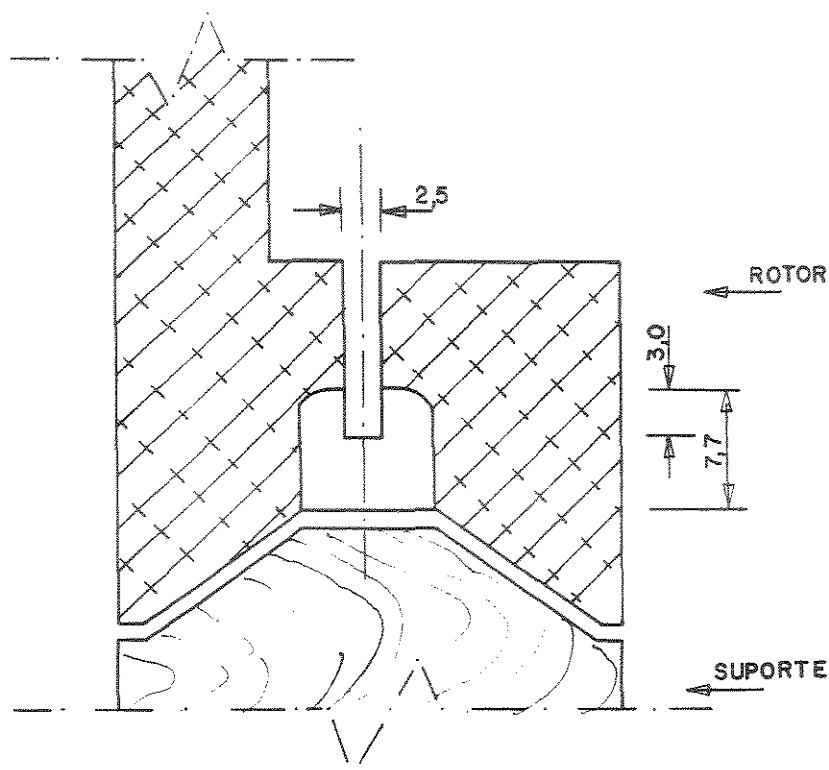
Vista em corte do rotor representando a fenda pela qual se desloca o disco do ejetor e a posição do suporte.
